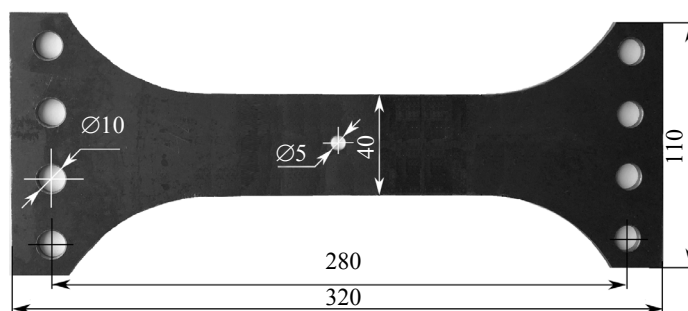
Форма и габаритные размеры образцов типа ЦО толщиной 3 мм.
